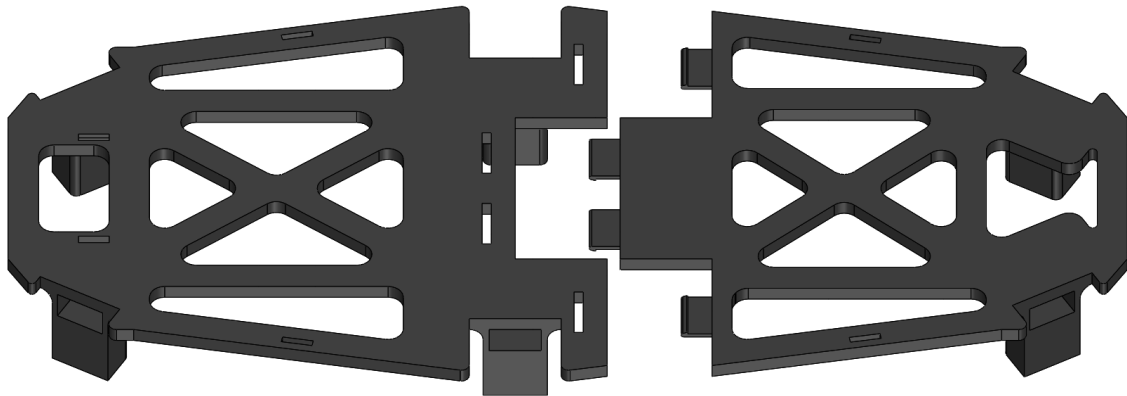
Vista explosionada de la parte del chasis superior. A la derecha chasis superior trasero y a la izquierda el delantero.
